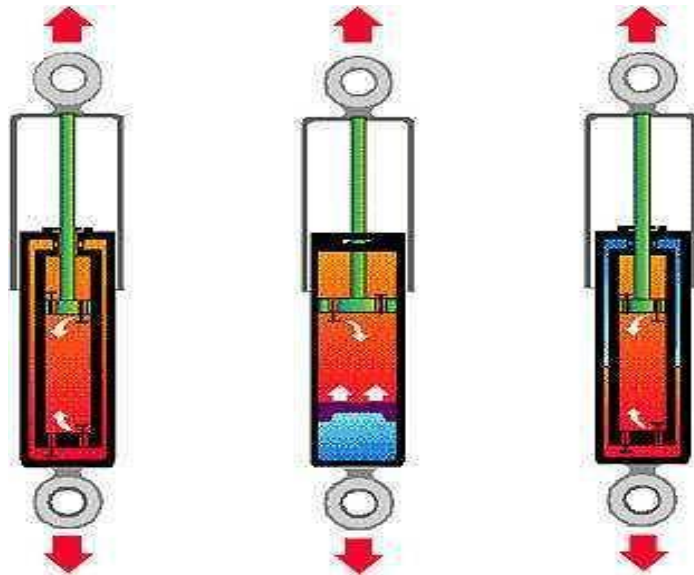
Пристрій телескопічний одно й двохтрубного амортизатора газомасляного типу
